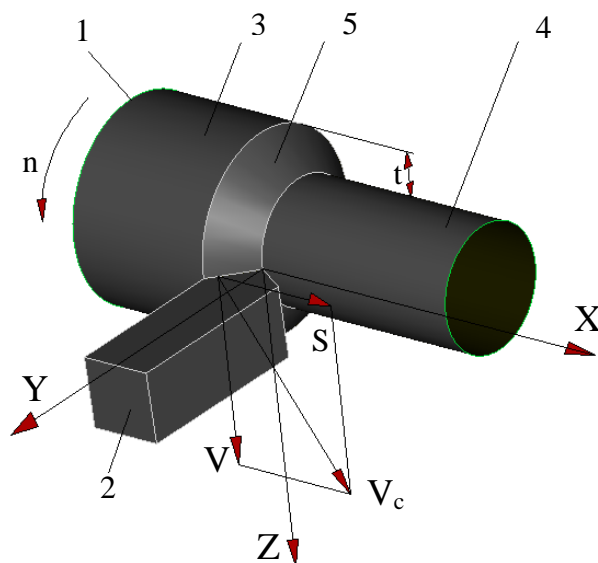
Кинематическая схема продольного точения: 1 – заготовка; 2 – резец; 3 – обрабатываемая поверхность; 4 – обработанная поверхность; 5 – поверхность резания; n – число оборотов заготовки; V – скорость резания; S – скорость движения подачи; V_c – результирующая скорость; t – глубина резания
